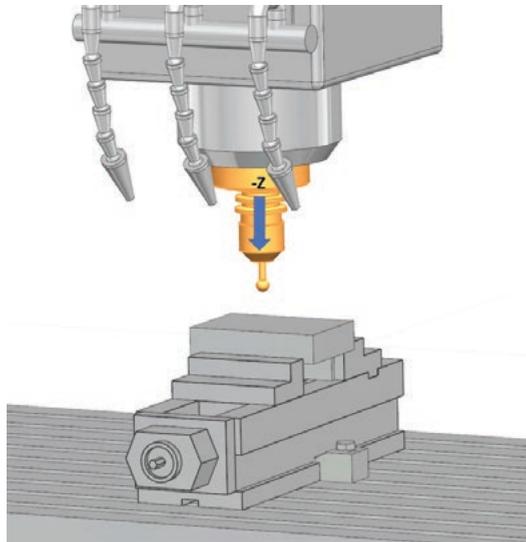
Vermessung des Werkstücks in Z-Richtung
